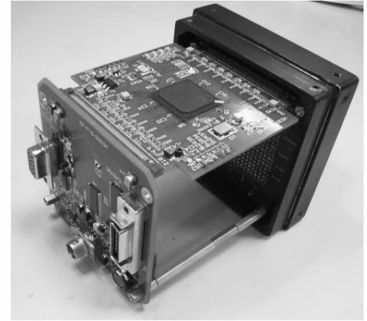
高帧频 CMOS 数字摄像机 PCB 实物图
